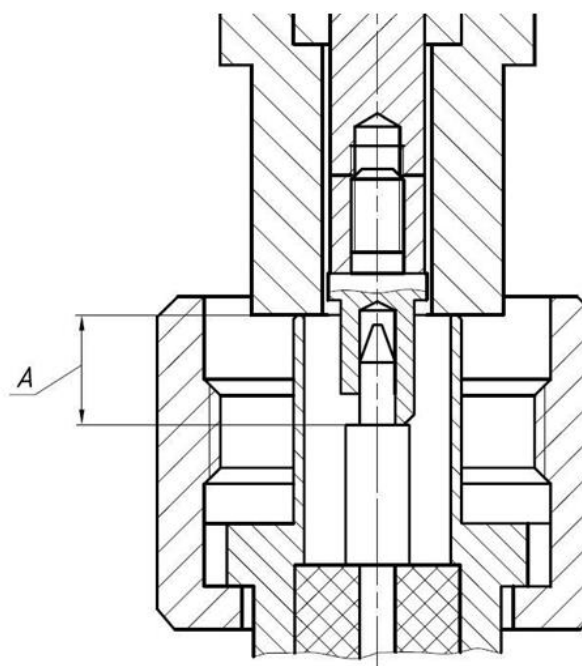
Проверка размера «А» соединителя «вилка»
